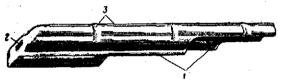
Крышка ствольной коробки: 7 — ступенчатый вырез; 2 — отверстие; 3 — ребра жесткости
